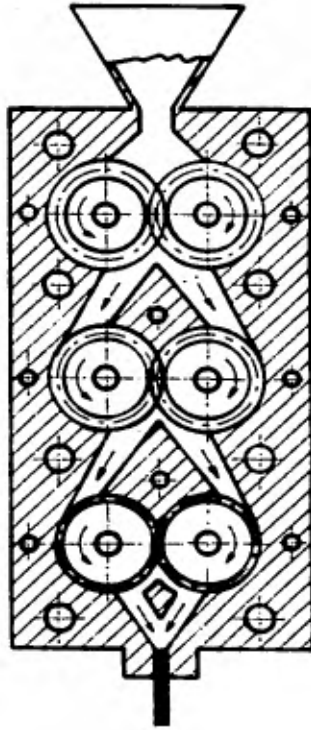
EXTRUSORA DE ENGRANAJES DE PASQUETTI.
